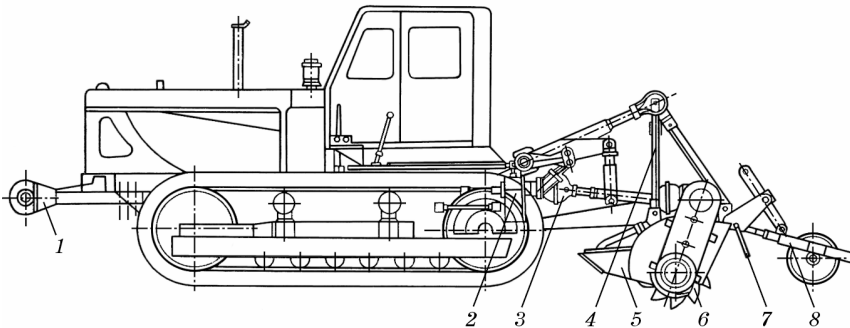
Конструктивна схема фрезерної машини ФКН-1,7:
